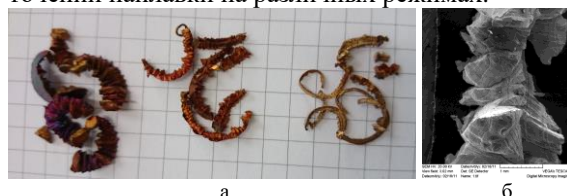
Форма стружки при точении наплавки резцом Т15К6 (а) — $v = 2,6$ м/с, $t = 1$ мм, $S =$ (справа налево 0,12, 0,25, 0,6 мм/об), (б) — вид стружки с боковой стороны
